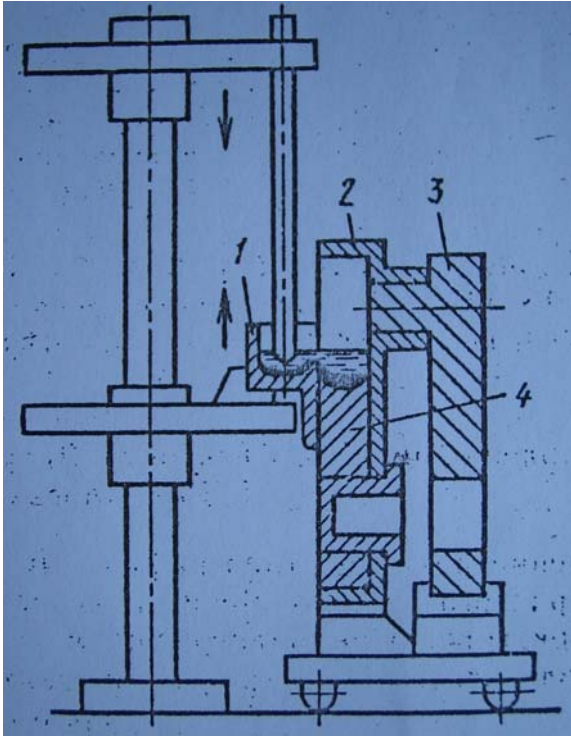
Схемы выплавки кривошипа коленчатого вала судового дизеля способом ЭШЛ.
